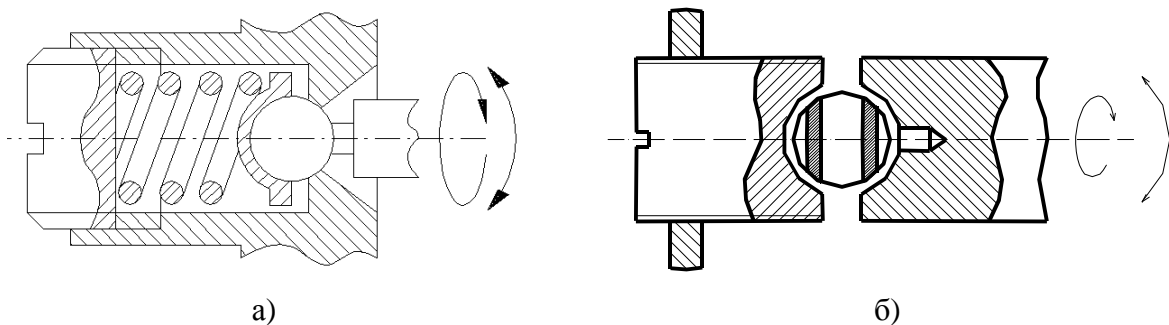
Кульові опори: а – плаваюча кульова опора; б– використання як опори шарикопідшипника
